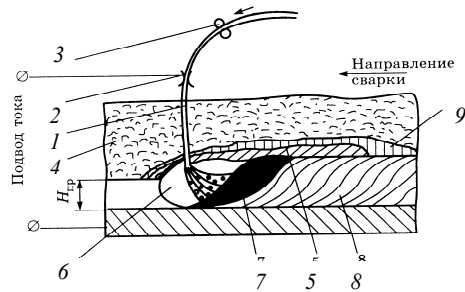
Схема процесса сварки под флюсом
